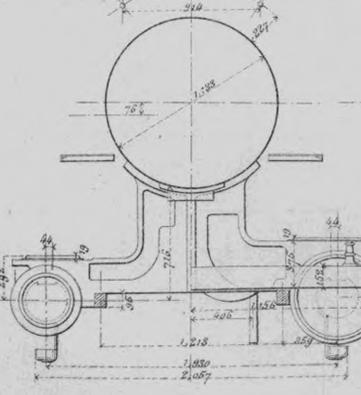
Demi-Élévation à l'arrière du tender. Demi-Coupe à travers la Plateforme.
